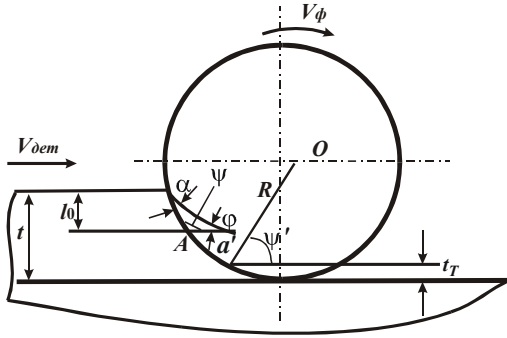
Схема для розрахунку кута  $\alpha$  під час циліндричного фрезерування
